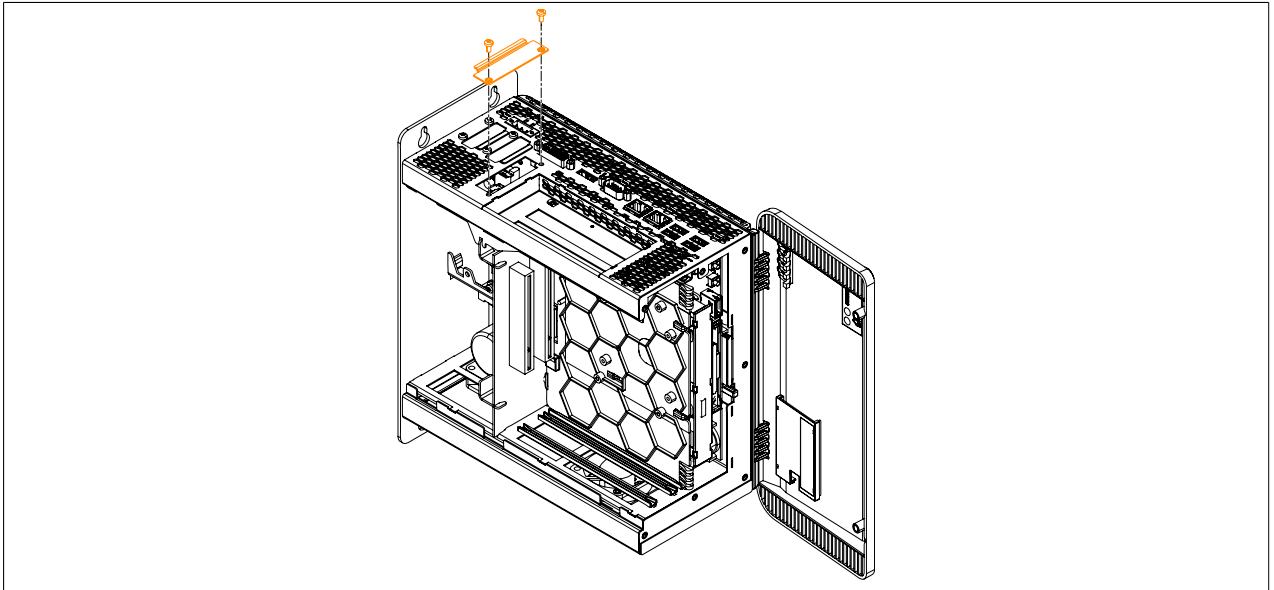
Torxschrauben und Blindabdeckung entfernen
